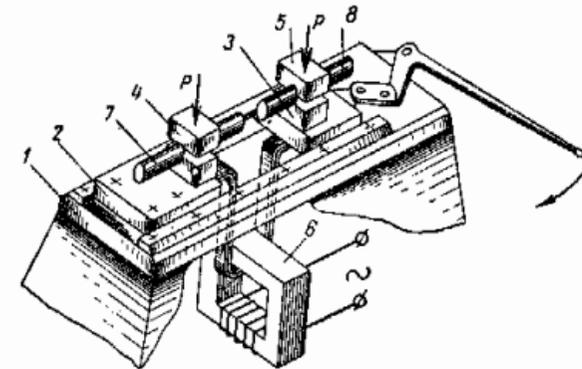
Схема машины для стыковой контактной сварки
